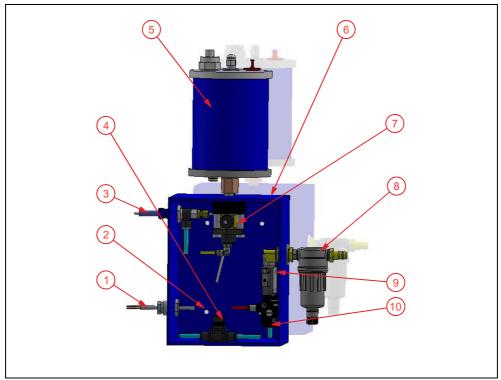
Hauptkomponenten des Minimalmengenschmiergeräts mit Messingpumpe
